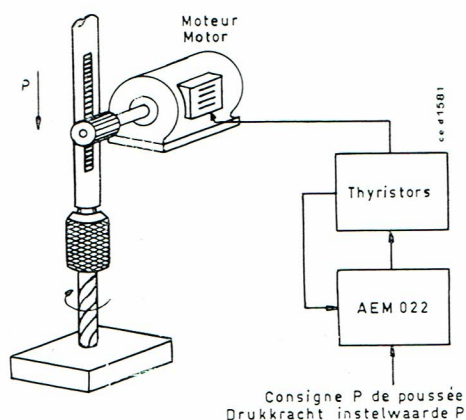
Poussée constante d'une mèche sur une pièce à forer
